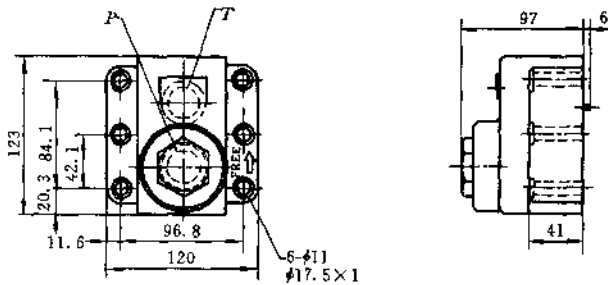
CRG-10 型直角双向阀外形尺寸
